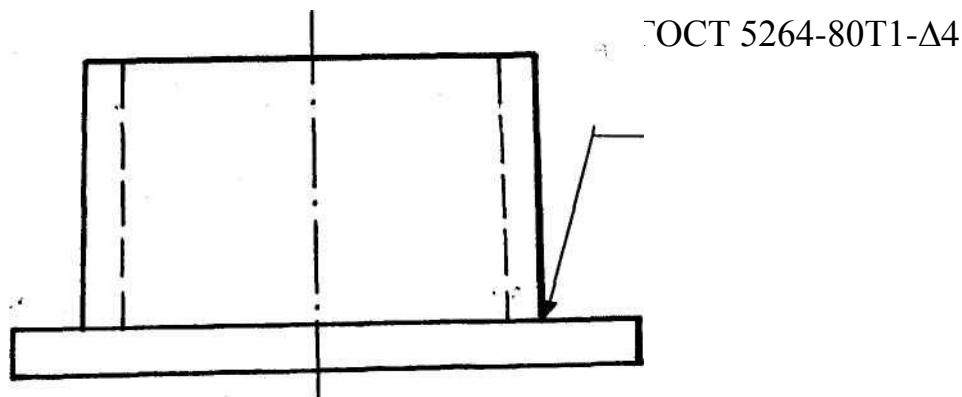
Эскиз сварного соединения заглушки с трубой
